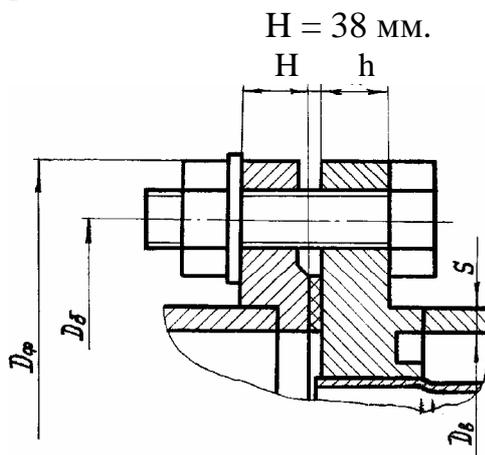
Конструкция фланцевого присоединения крышки к корпусу аппарата
